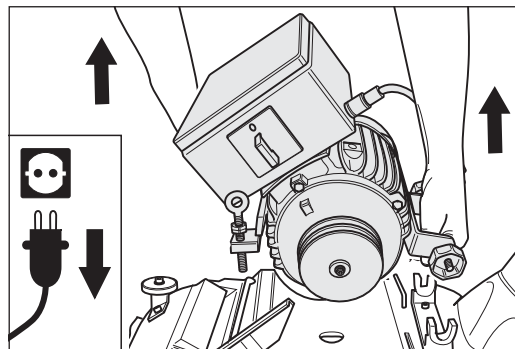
Den Motor vom Maschinengehäuse abnehmen.
